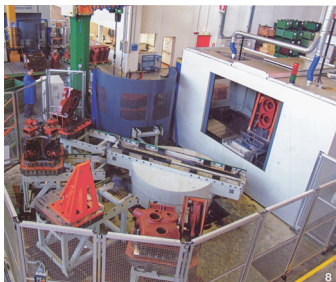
Цех для механічної обробки корпусів редукторів великих розмірів
